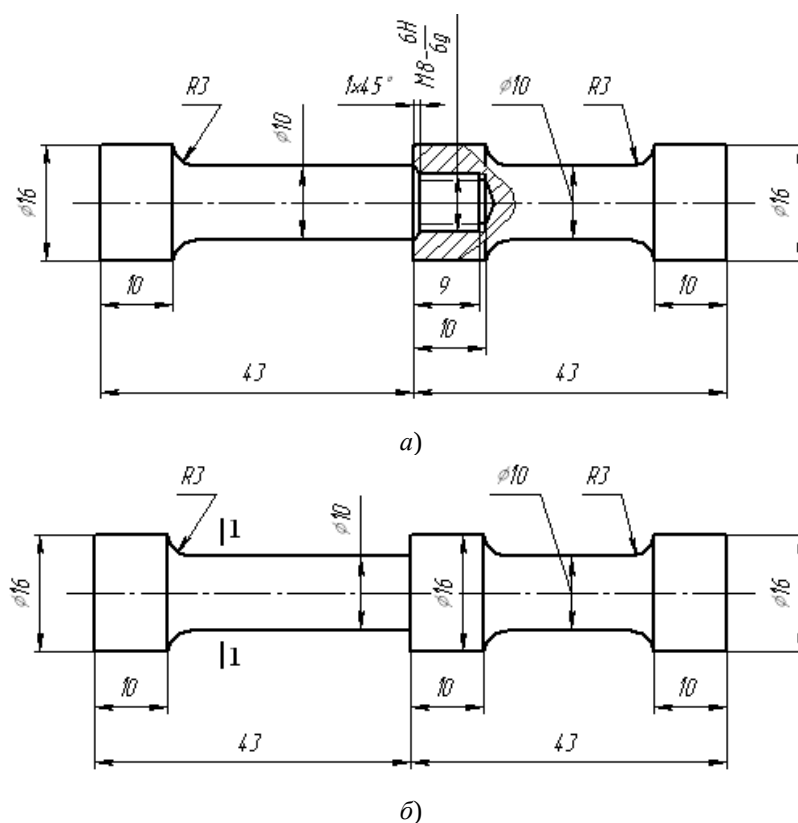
Эскиз соединения резьбовых деталей при исследовании жесткости резьбовых соединений:
